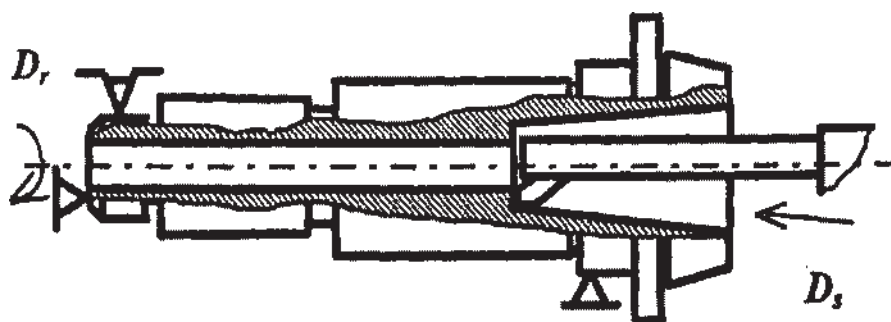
Схема обработки внутренних конических поверхностей на токарном станке с ЧПУ
